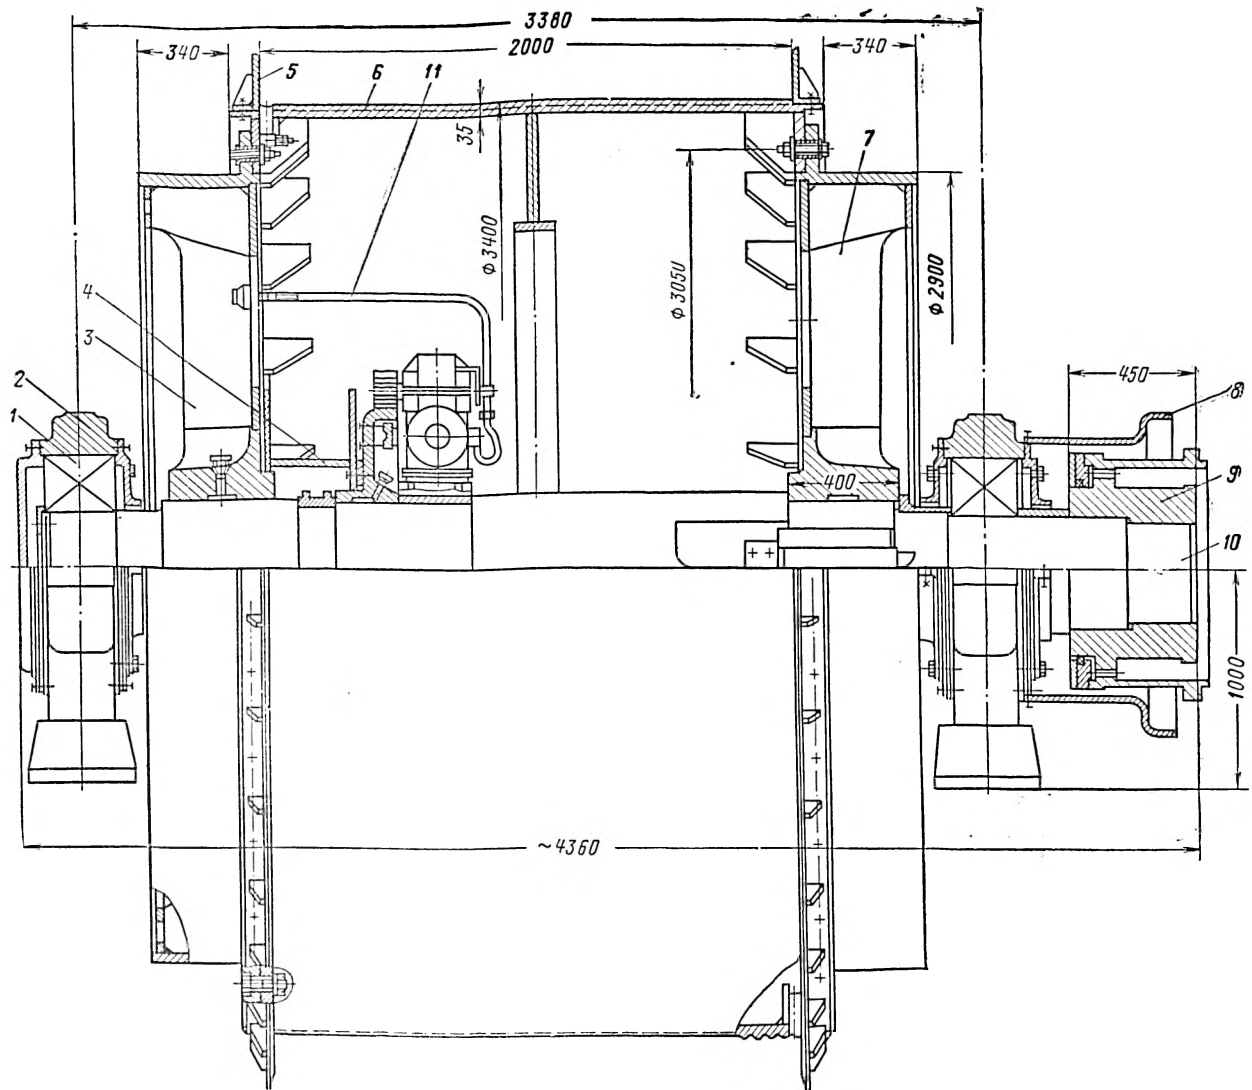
Сборка главного вала машины Ц-3,5×2А:
